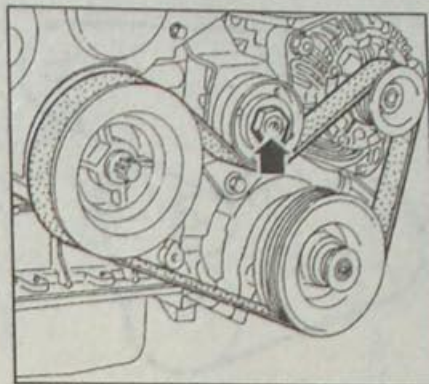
Расположение болта крепления ролика натяжного устройства ремня привода навесных агрегатов на автомобиле с дизельным двигателем без системы кондиционирования воздуха
